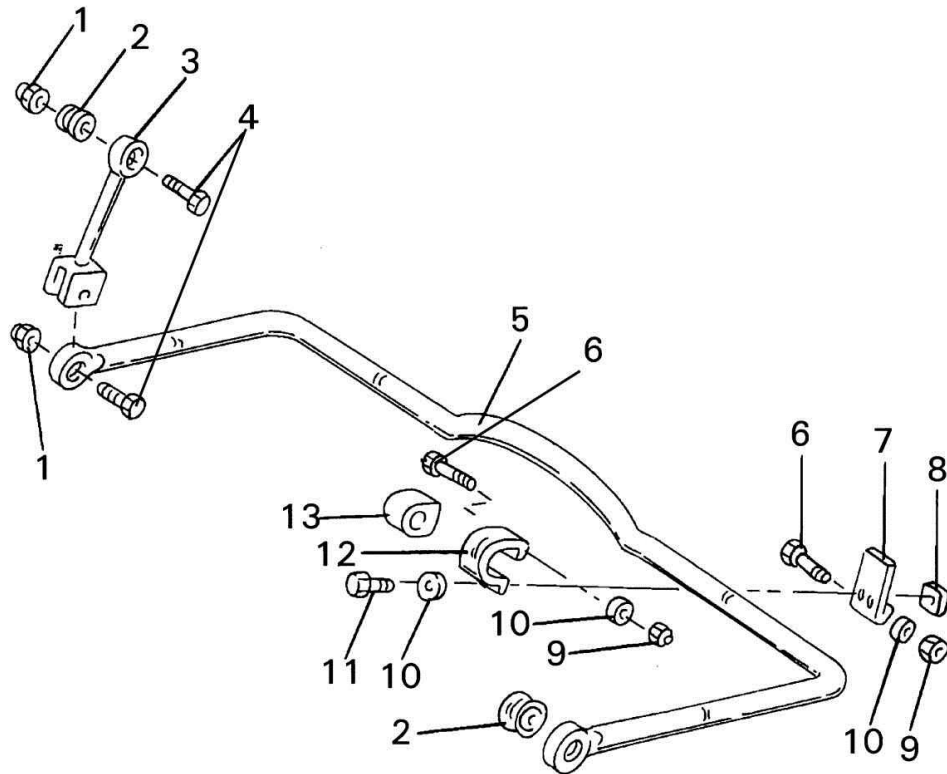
Деталі для кріплення штанги стабілізатора поперечної стійкості:
